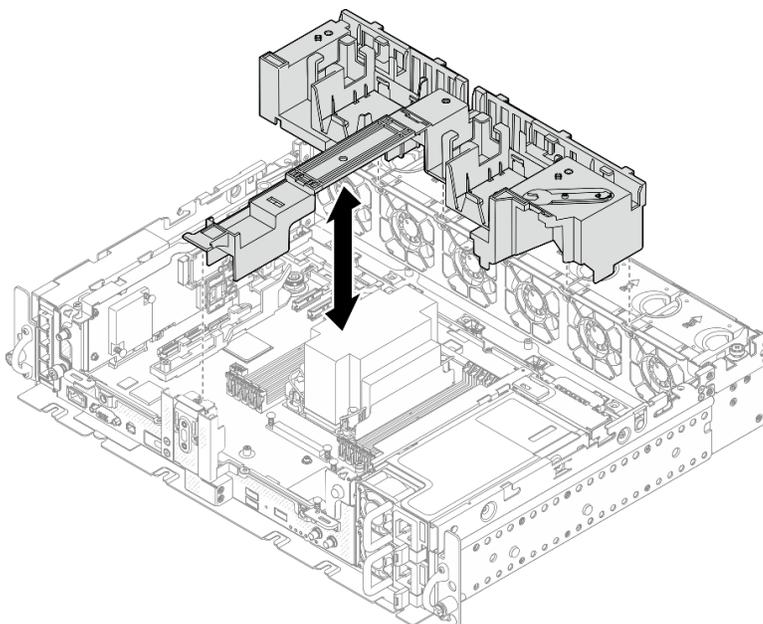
Entfernen der 360-mm-Luftführung mit Adaptern mit voller Länge
